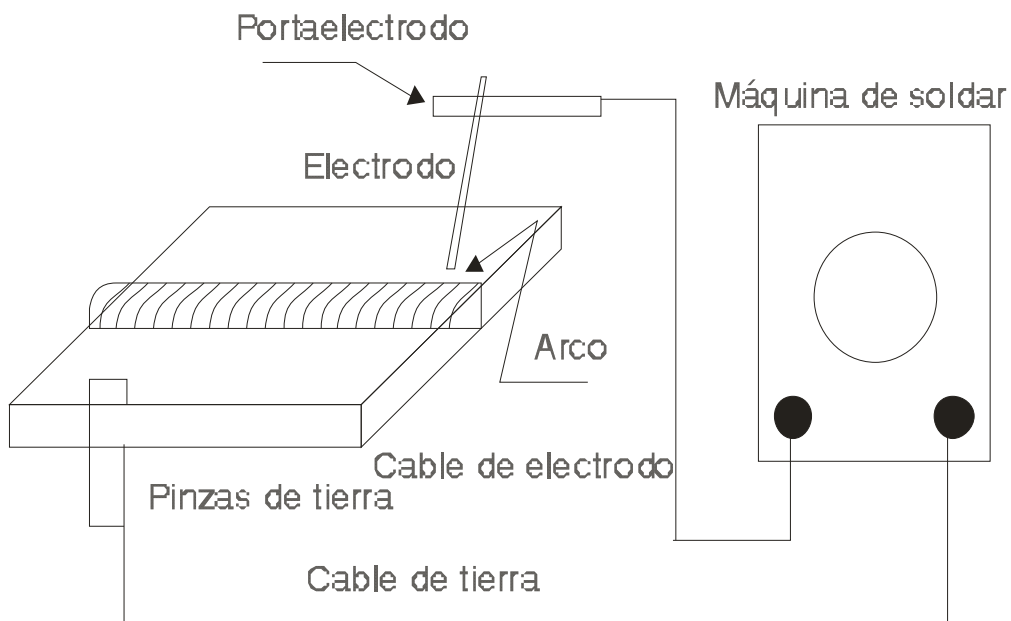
Soldadura por arco eléctrico.
